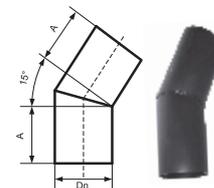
Отвод 15° сварной 2-х сегментный
